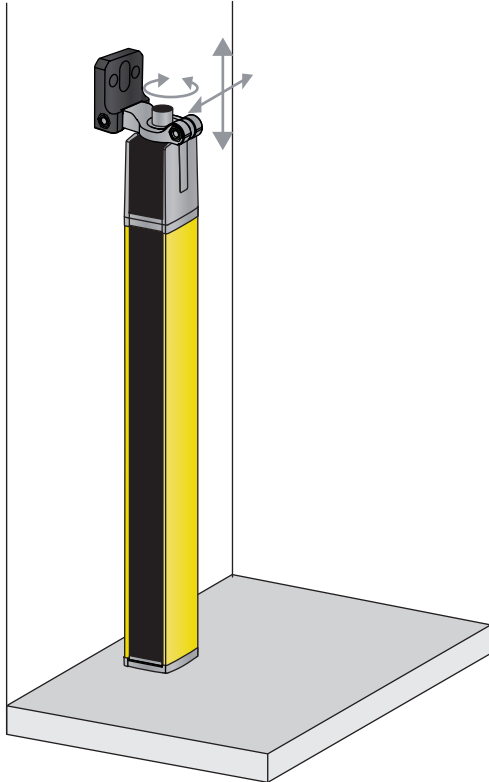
Befestigung direkt auf dem Maschinentisch
